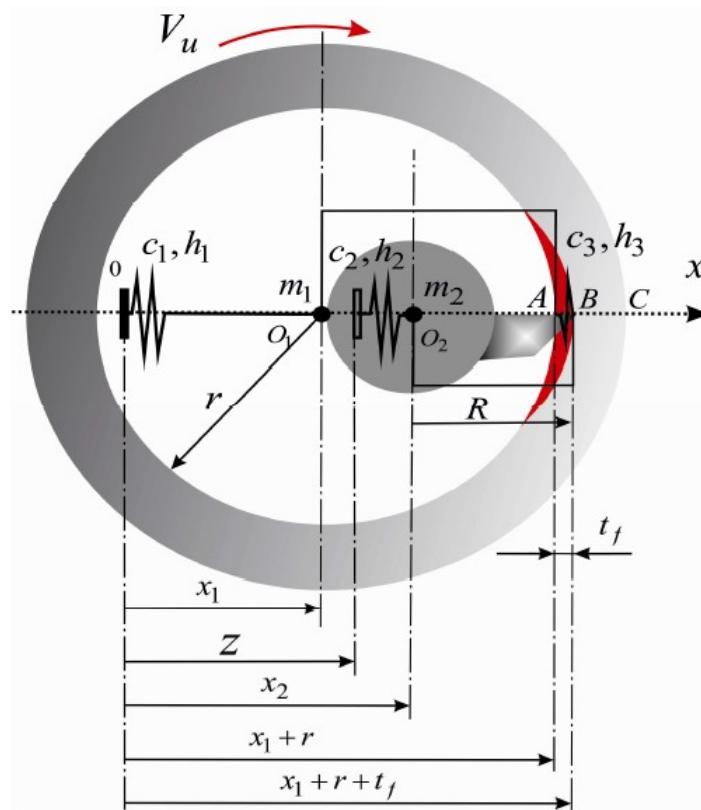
Розрахункова схема процесу розточування на токарному верстаті
